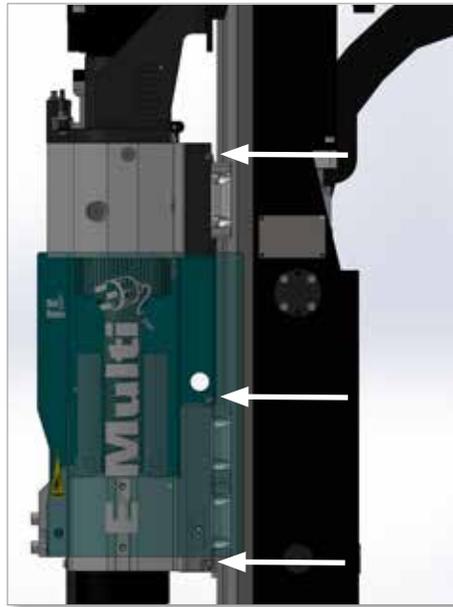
Schmierpunkte für die Linearführungen (insgesamt 6)
